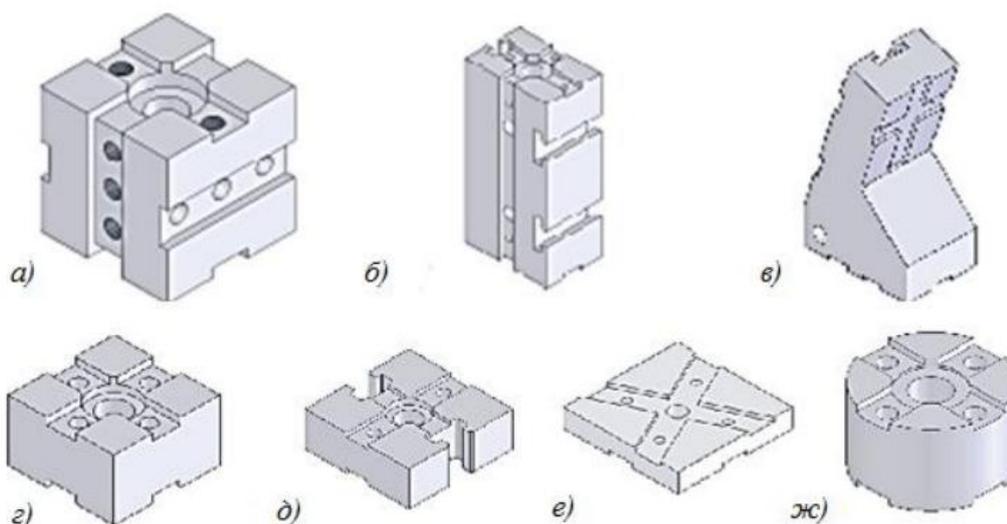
Корпусные детали: а) опора квадратная, б) опора прямоугольная,
